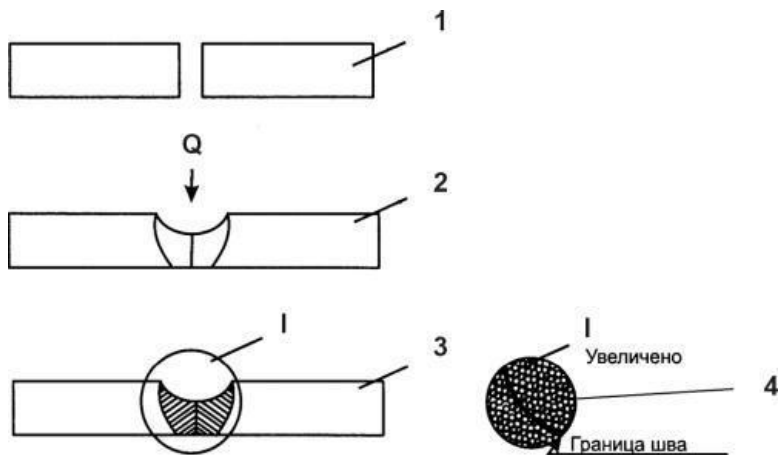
Схема стадий образования соединения сваркой плавлением:
